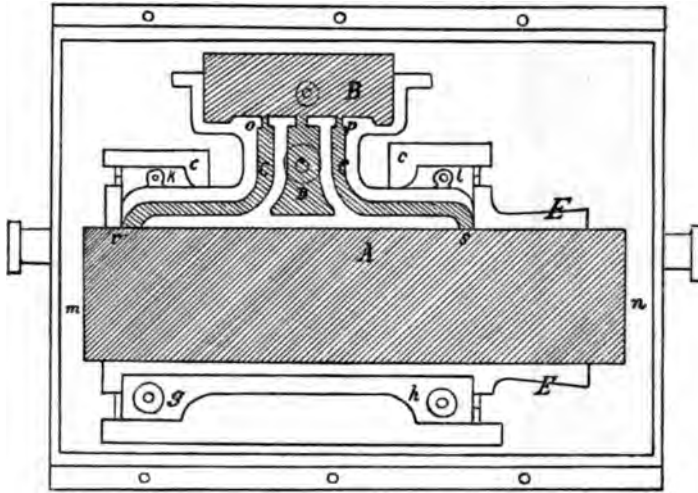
Grundriß des unteren Formkastens mit eingelegten Kernen.
